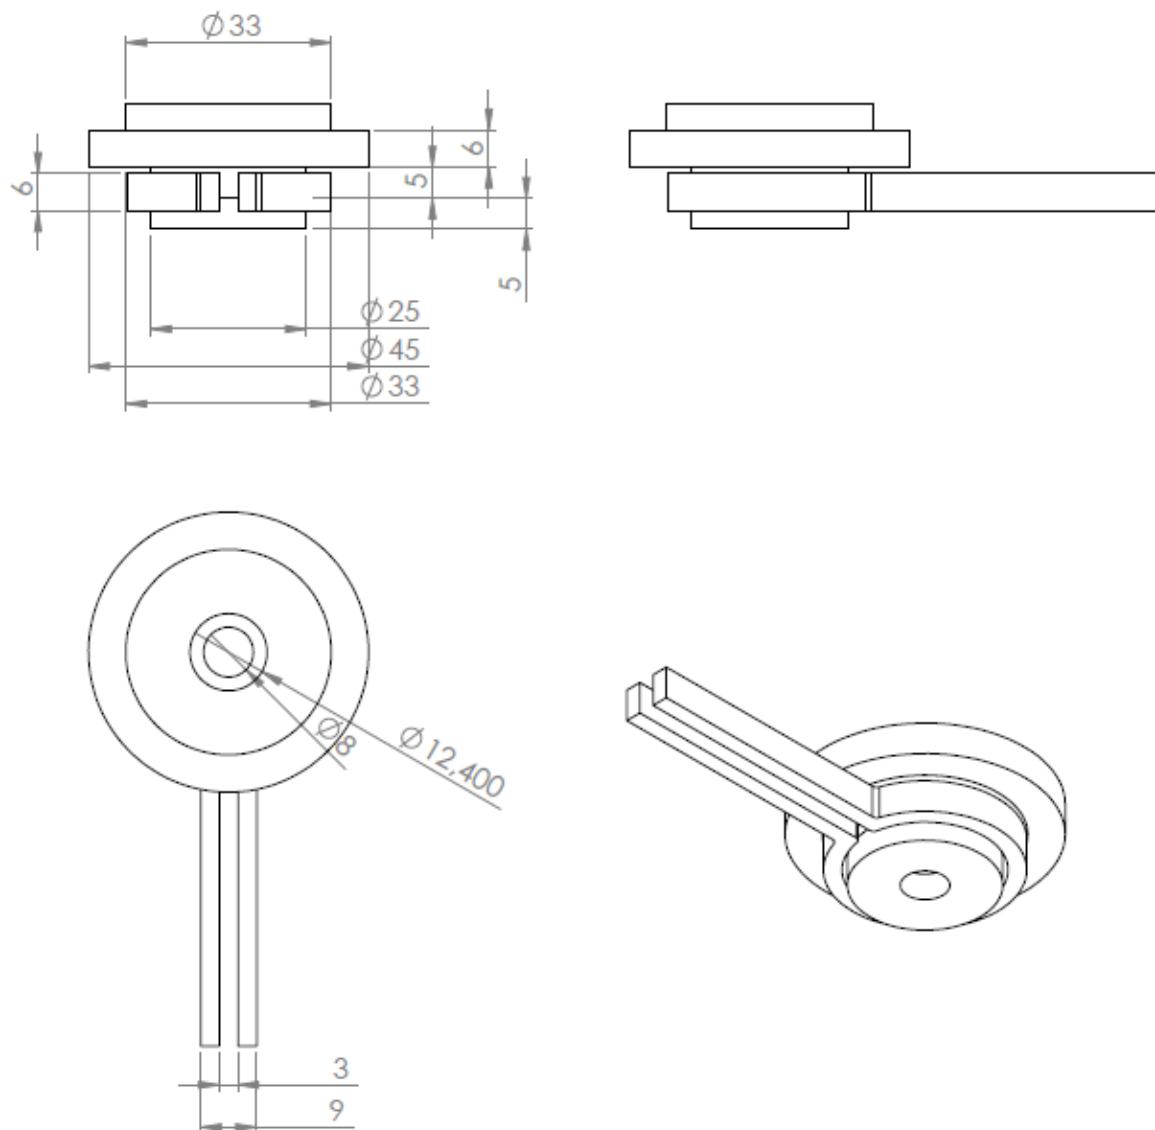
Dessin du montage de la portée de roulement et de l'inducteur
